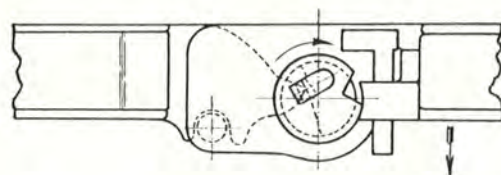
Vue en plan et coupe de la bèle Jadot déverrouillée.
